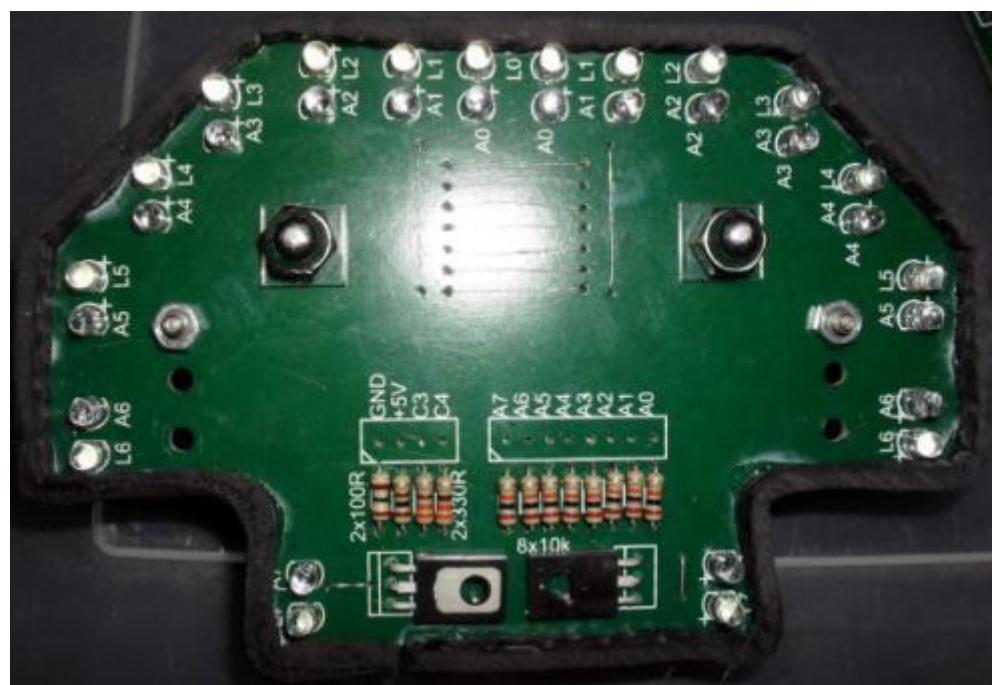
Realisasi PCB Microcontroller Unit (MCU)
